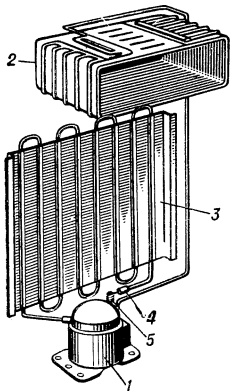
Компрессионный холодильный агрегат: 1 — компрессор; 2 — испаритель; 3 — конденсатор; 4 — фильтр-осушитель; 5 — дроссельное устройство (капиллярная трубка).
